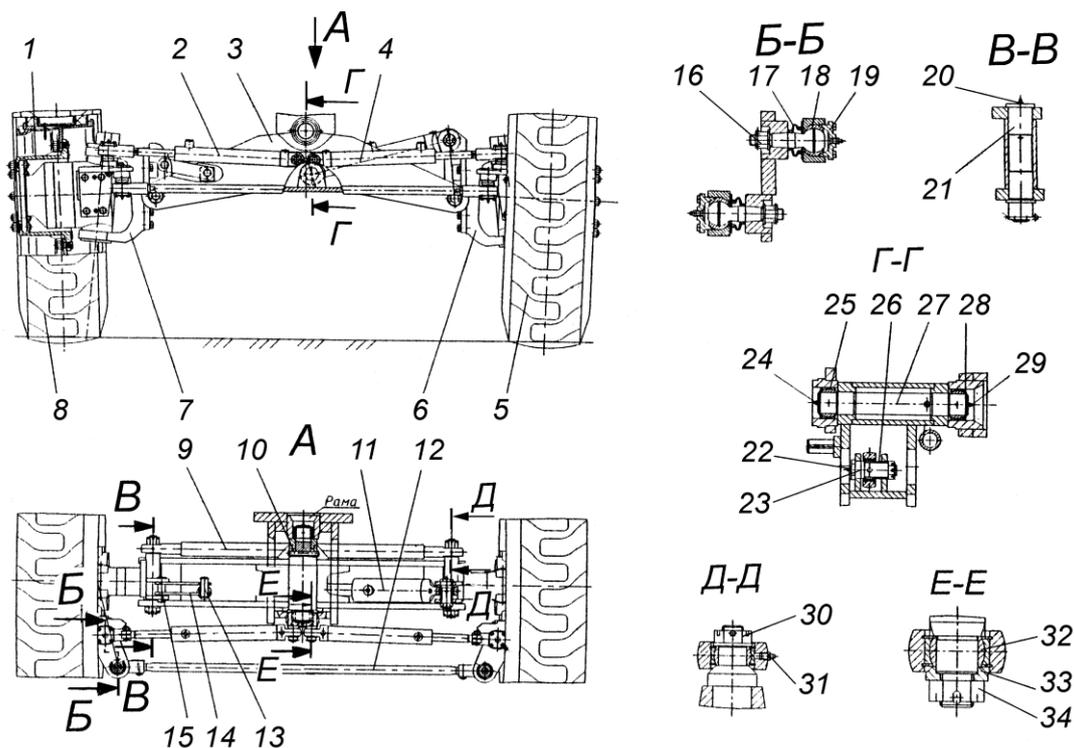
Передний мост автогрейдера ГС-25.09: 1 – ступица; 2, 4, 11 – гидроцилиндры; 3 – балка; 5, 8 – колеса; 6, 7 – гидромоторы; 9, 12 – штанги; 10, 13 – пальцы; 14 – планка; 15 – защелка; 16, 30, 34 – гайки; 17 – манжета; 18 – вкладыш; 19, 28, 33 – крышки; 20, 23, 24, 29, 31 – масленки; 21, 22, 27 – оси; 25, 32 – подшипники ШС; 26 – втулка
